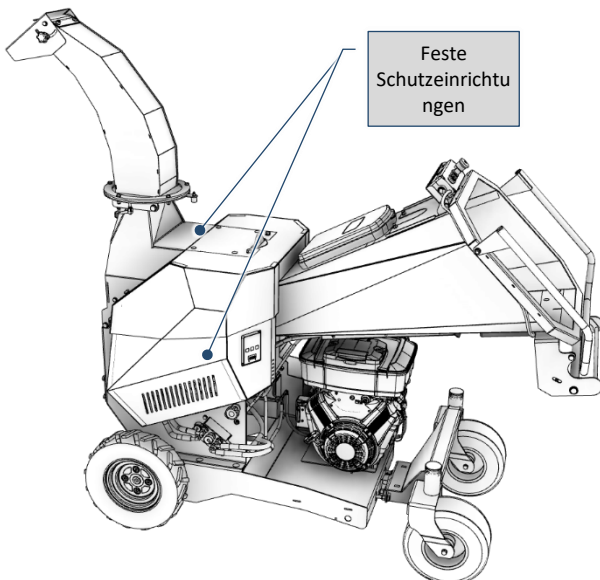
Feste Schutzeinrichtungen der Maschine (Linke Seitenansicht)
